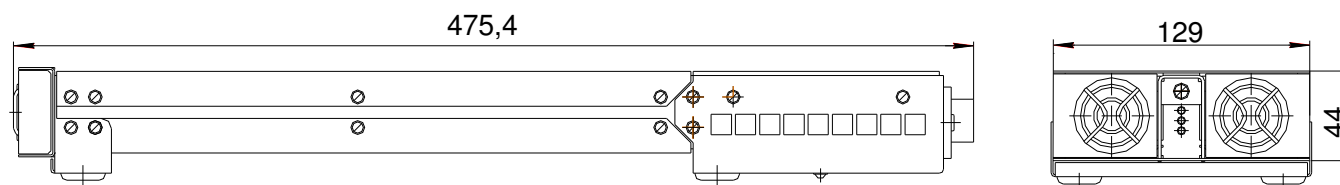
Габаритный чертеж ИЦ-700 БП-19
